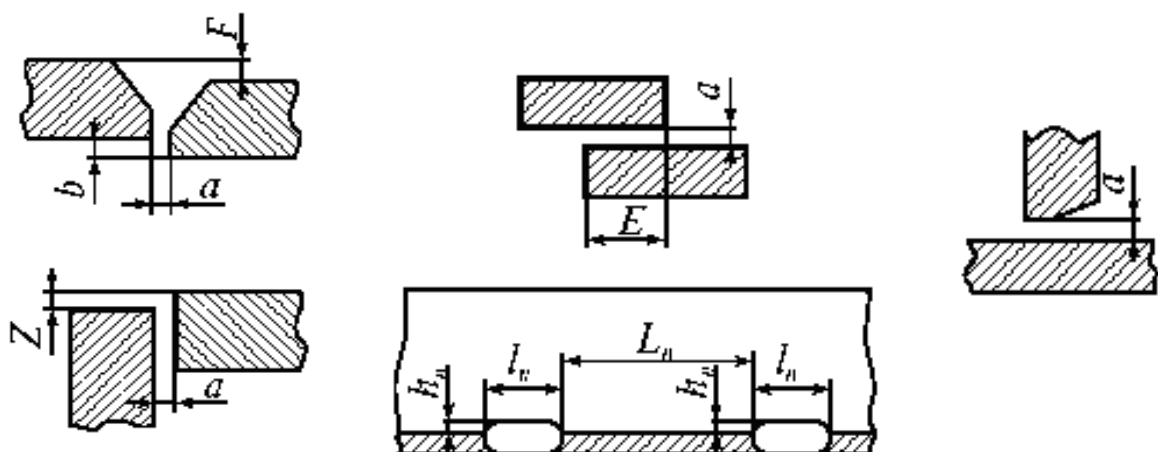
Контролируемые параметры сварных соединений
